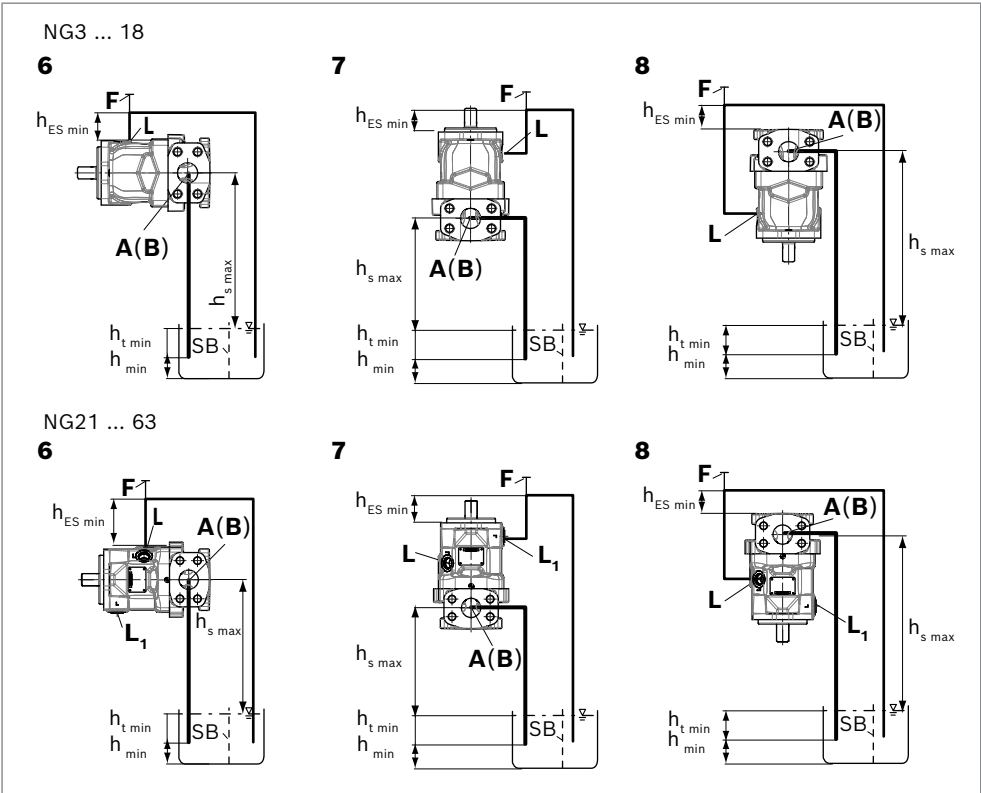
Übertankeinbau A10FZO mit Einbaulage 6–8
